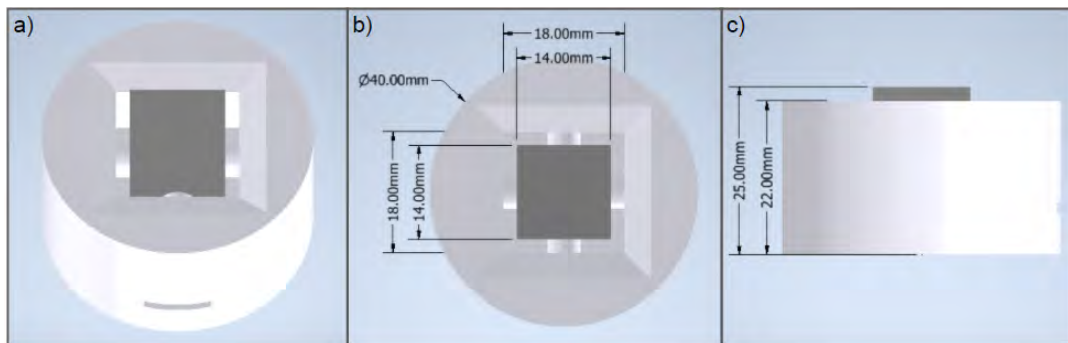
Ensamblaje del mecanismo de aluminio y de la estructura externa. a) Vista isométrica. b) Vista superior con medidas. c) Vista lateral con medidas.
